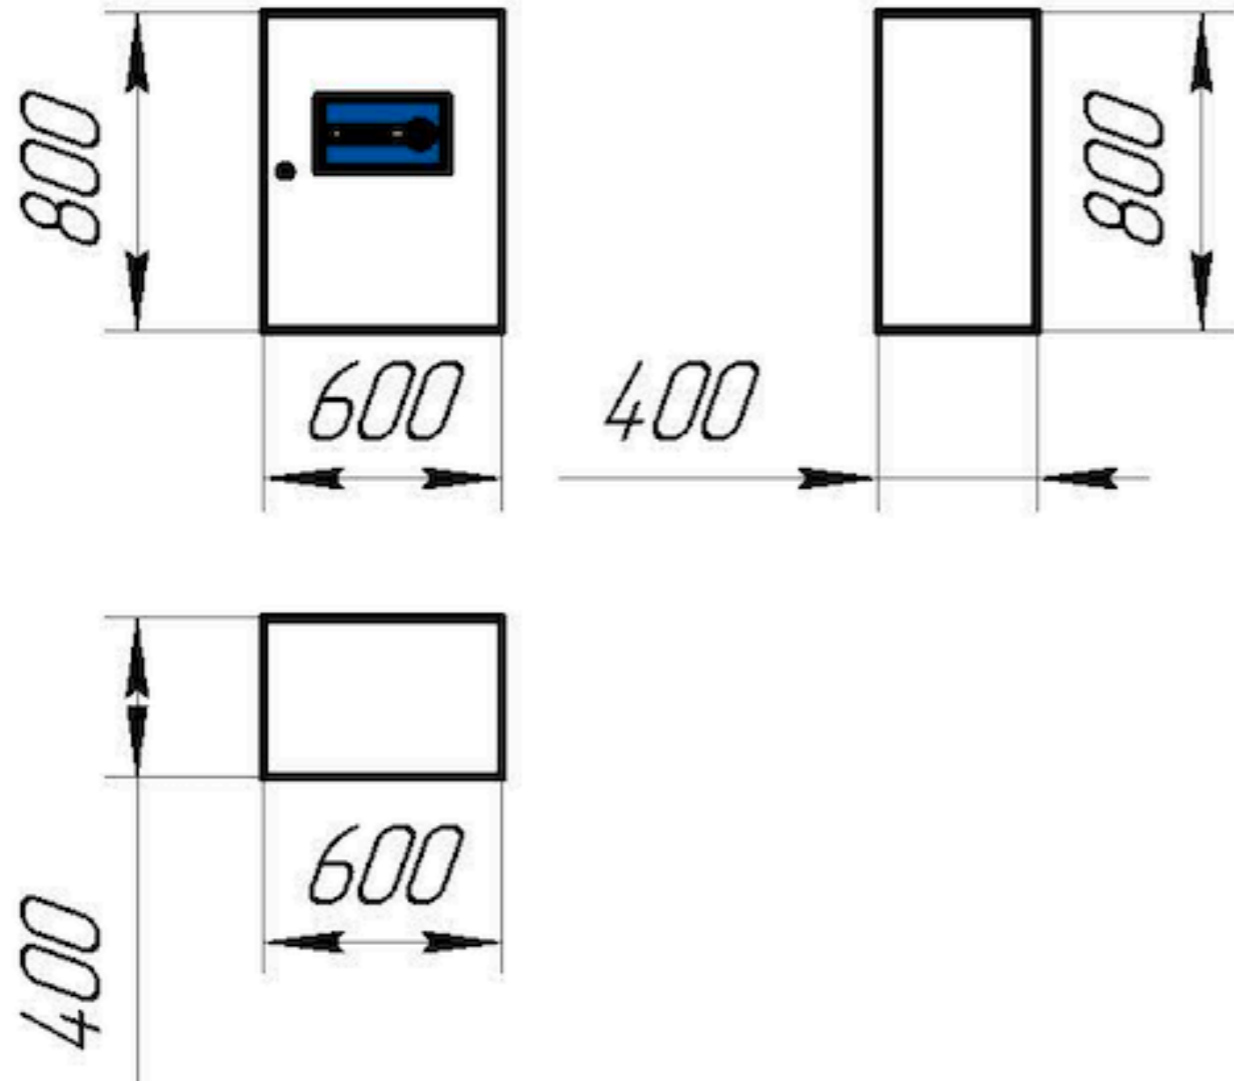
Габаритный чертеж устройства автоматического ввода резерва
